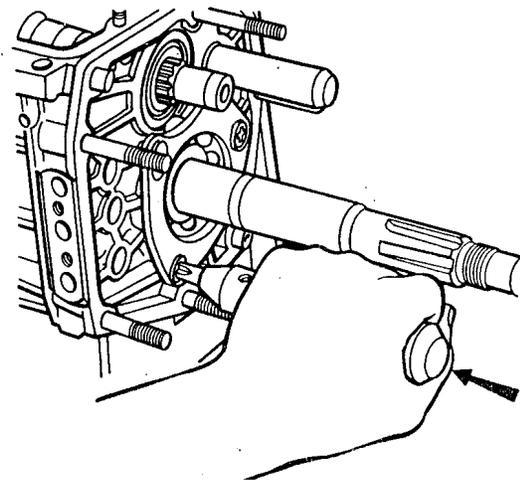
Desenrosque de los tornillos de sujeción de la placa de retención del cojinete intermedio del árbol secundario con ayuda de un destornillador de berbiquí.
